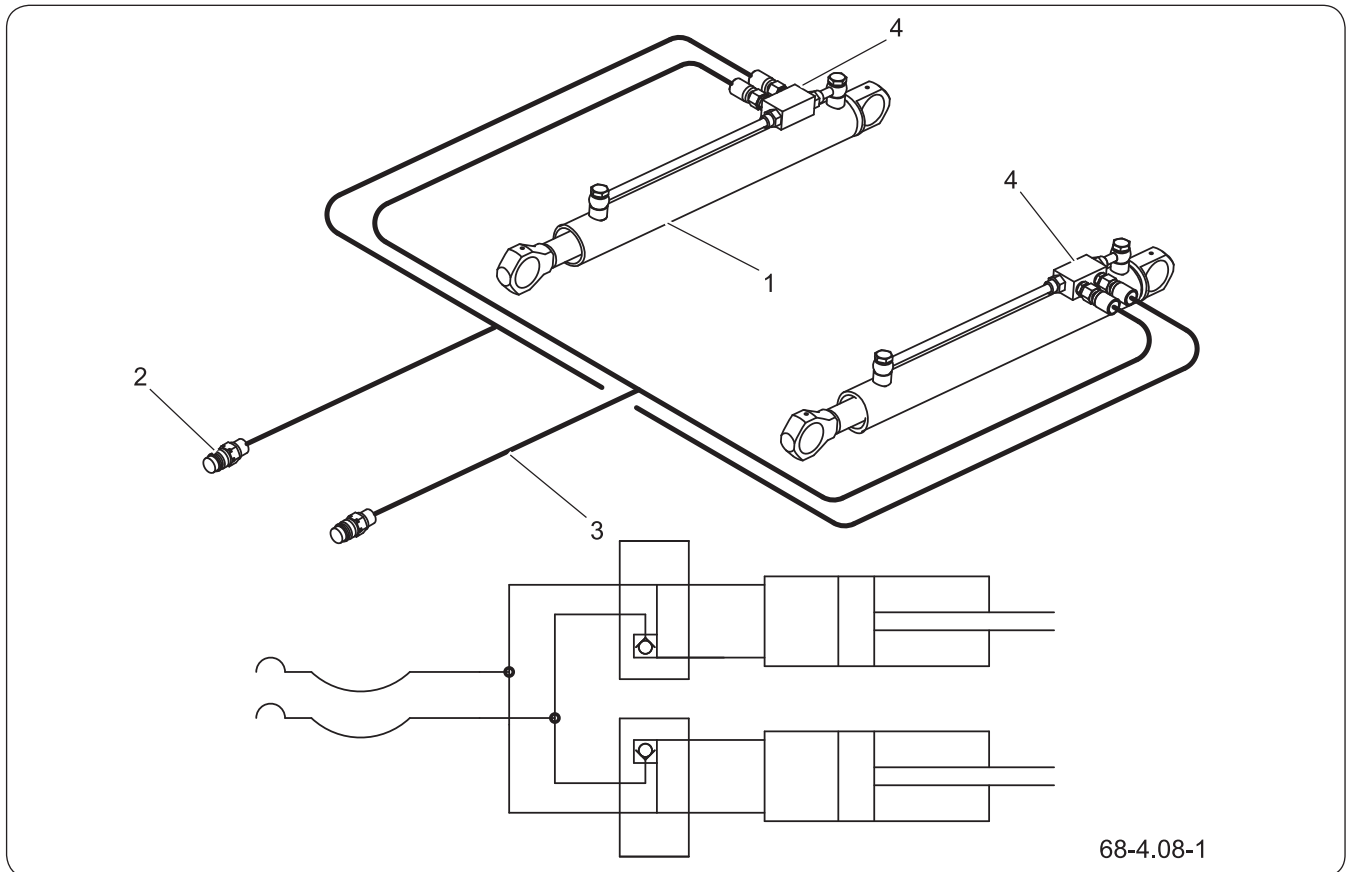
Aufbau und Schema der Hydraulikanlage für die SILO-Rückwandklappe
